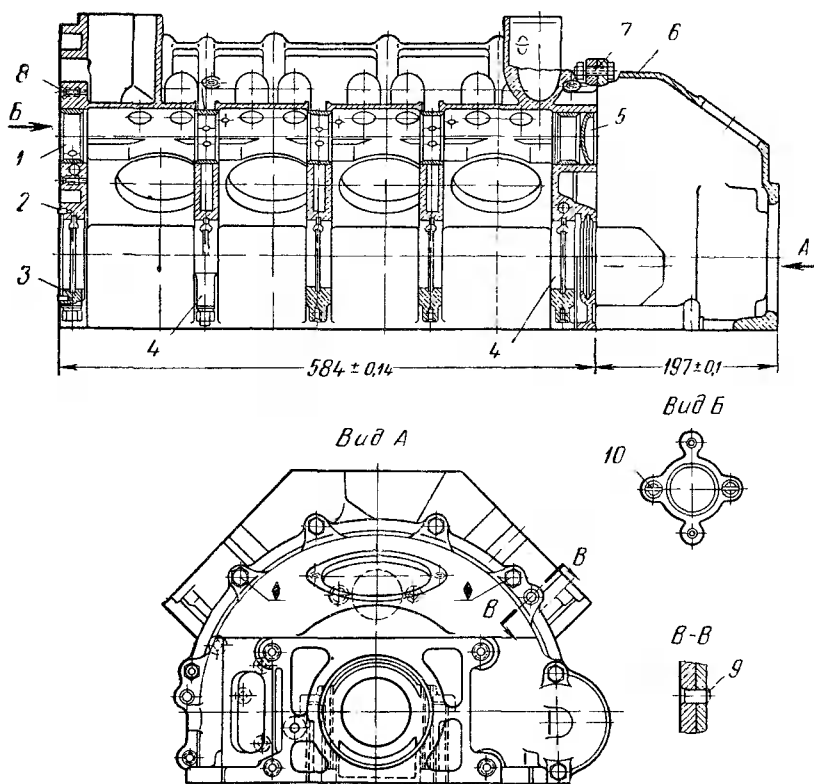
Детали, входящие в сборочный узел (блок цилиндров в сборе) двигателей ЗМЗ-53
